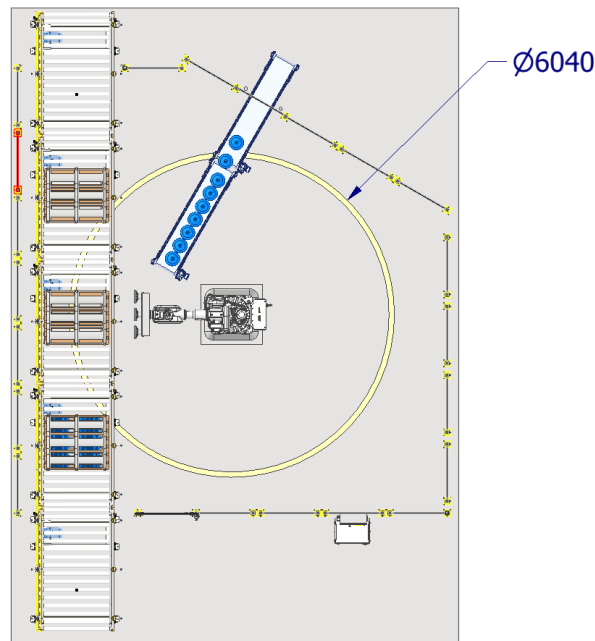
Vista planta de celda de paletizado - Manipulador ABB IRB 5710
